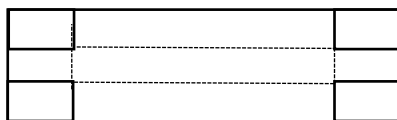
Схема изготовления из прямоугольной заготовки с указанием ее размеров
